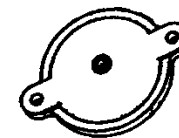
Крышка подшипника КИР.02.0.1003
